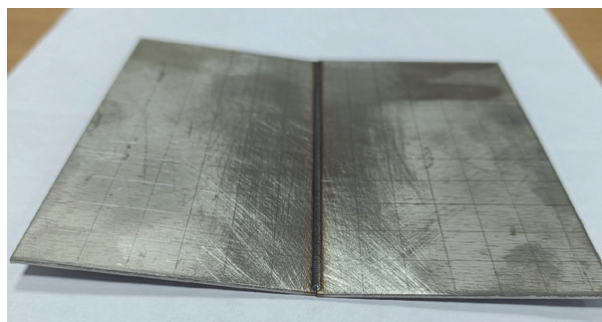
Пластины из 12X18H10T сваренные лазерной сварки
